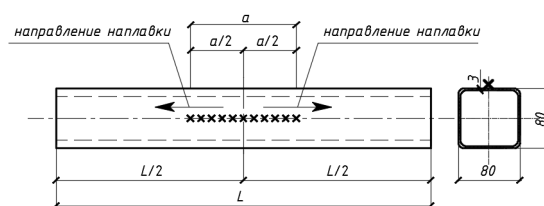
Схема расположения и направления наплавки холостых валиков
